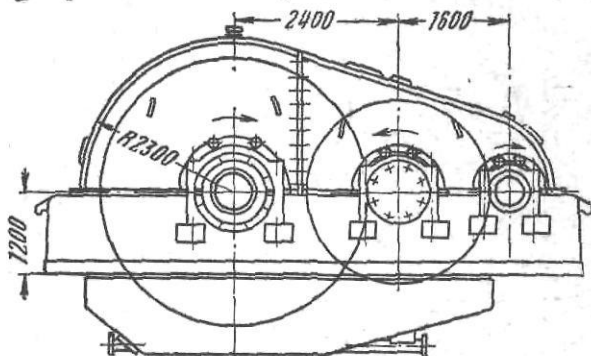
Двухступенчатый редуктор с цилиндрическими шестернями ЦД-4000
